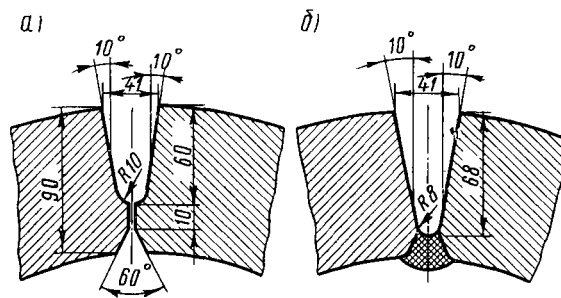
Форма разделки продольного стыка обечайки под многослойную сварку:
